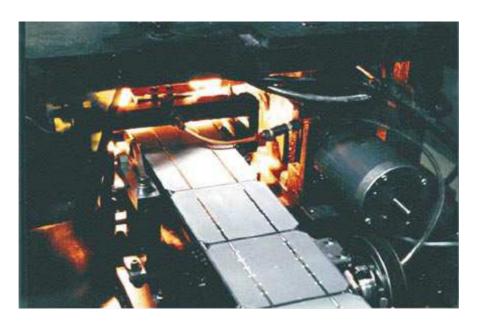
Proceso de soldadura de la rejilla metálica durante el ensamblaje del panel.
